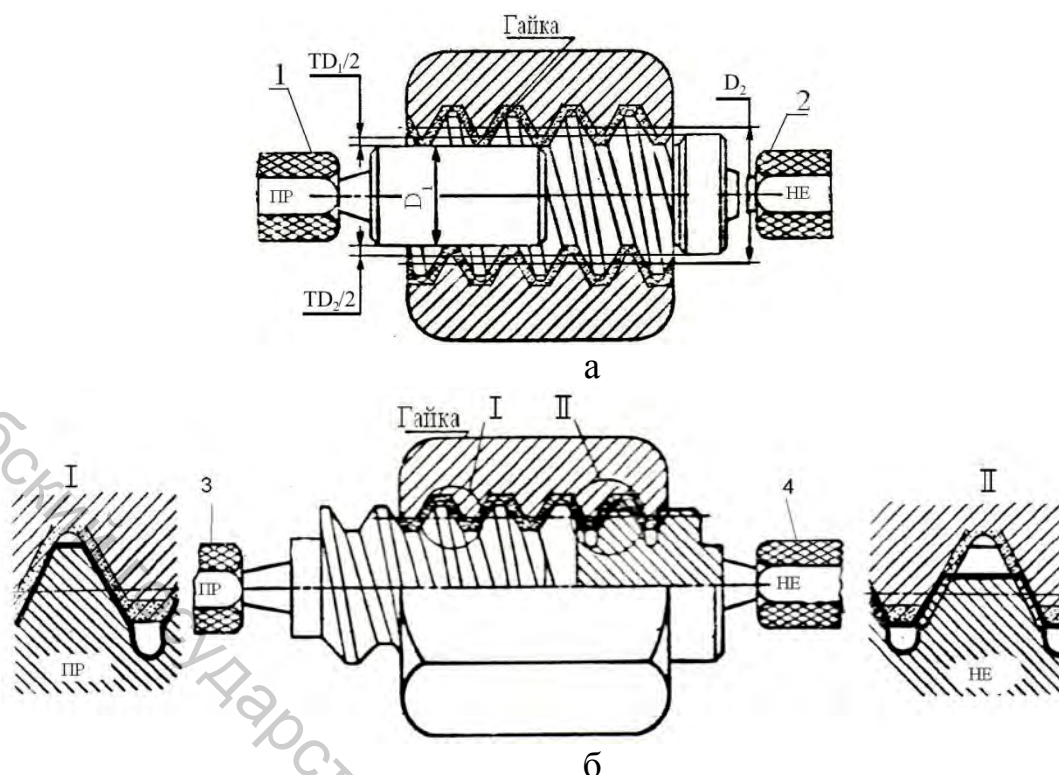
Схемы контроля допусков внутренней резьбы:
